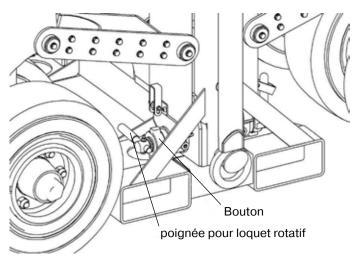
Dispositif Twist-Lock en position déverrouillée
